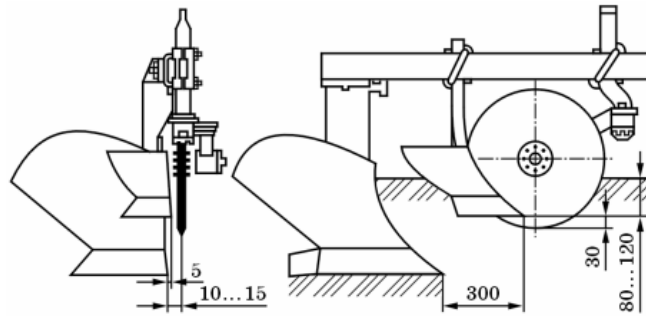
Схема взаємного розміщення дискового ножа та передпłużника
